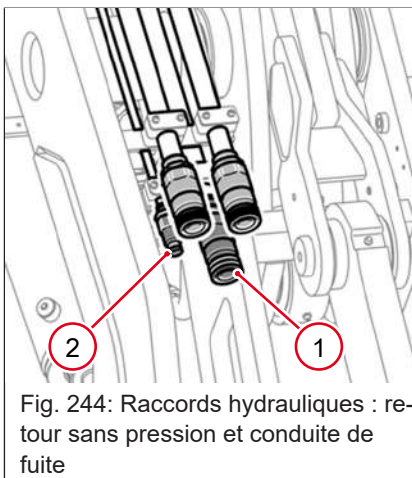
Raccords hydrauliques : retour sans pression et conduite de fuite
